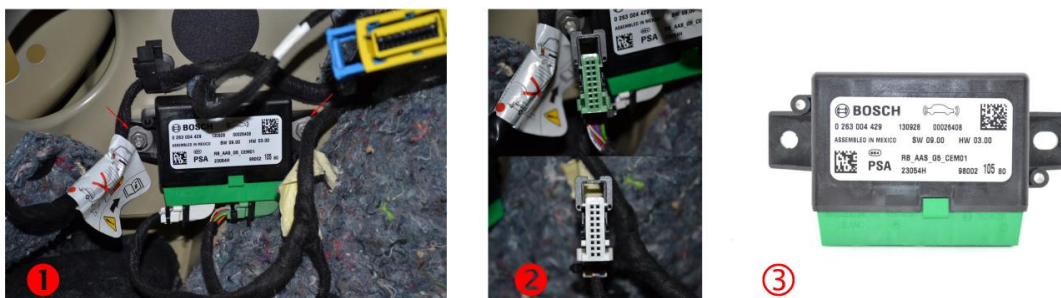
Bild 1: Verbau des Park Assist Steuergeräts im Fahrzeug. Bild 2: Stecker des Steuergeräts. Bild 3: Zerlegetiefe für die eHPV Bewertung.
